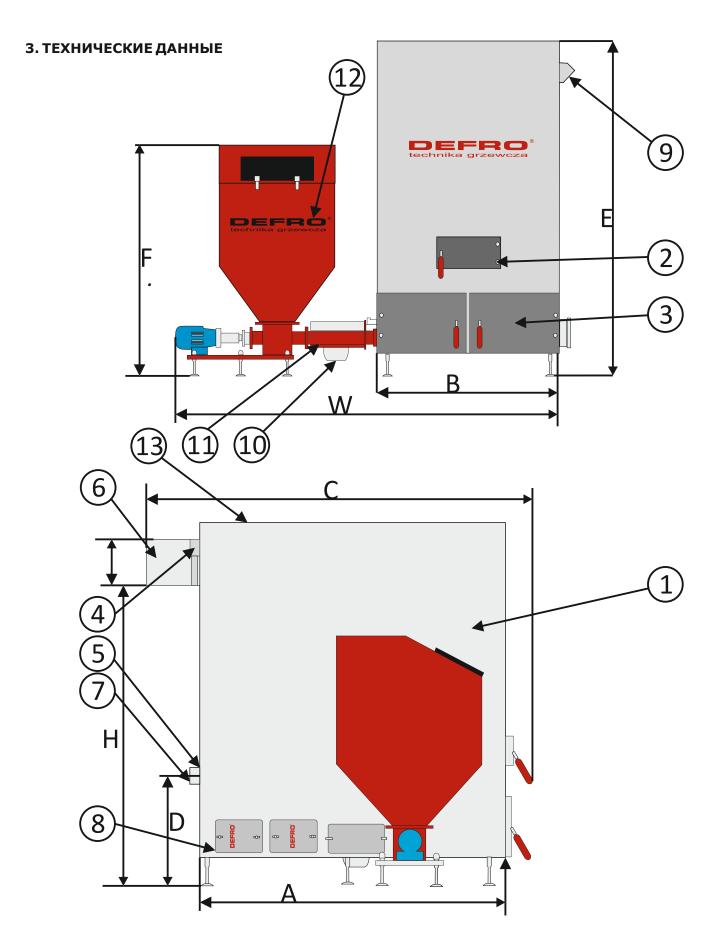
Основные элементы котлов типа DEFRO KOMPAKT MAX с оснащением: 1-стальной корпус с термоизоляцией; 2-очистные дверцы; 3-зольниковые дверцы; 4-питающий патрубок (2 шт.); 5-возвратный патрубок (2 шт.); 6-дымовой боров; 7-спусковой патрубок; 8-боковая очистка; 9-микропроцессорный регулятор; 10- вентилятор; 11-система подачи топлива с моторедуктором; 12-бункер на топливо; 13 - крышка для очистки.
